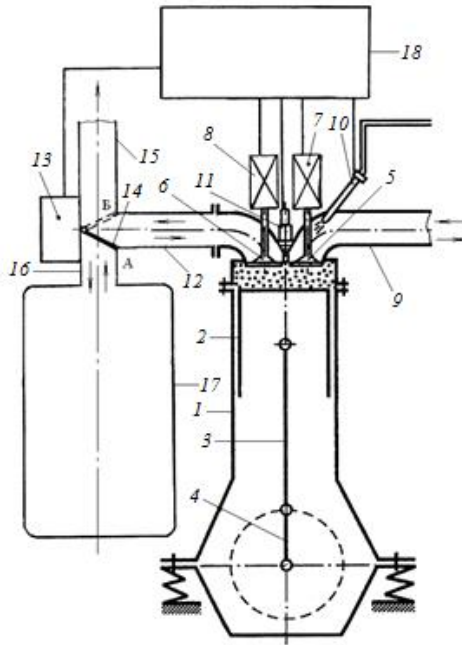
Схема силової установки: 1 – циліндр; 2 – поршень; 3 – кривошипно-шатунний механізм; 4 – колінчастий вал; 5 – клапан впускний; 6 – клапан випускний; 7, 8 – пристрої електромагнітного управління; 9 – впускний трубопровід; 10 – форсунка; 11 – свічка; 12 – випускний трубопровід; 13 – привід заслінки; 14 – поворотна заслінка; 15, 16 – трубопровід; 17 – ресивер; 18 – блок управління
